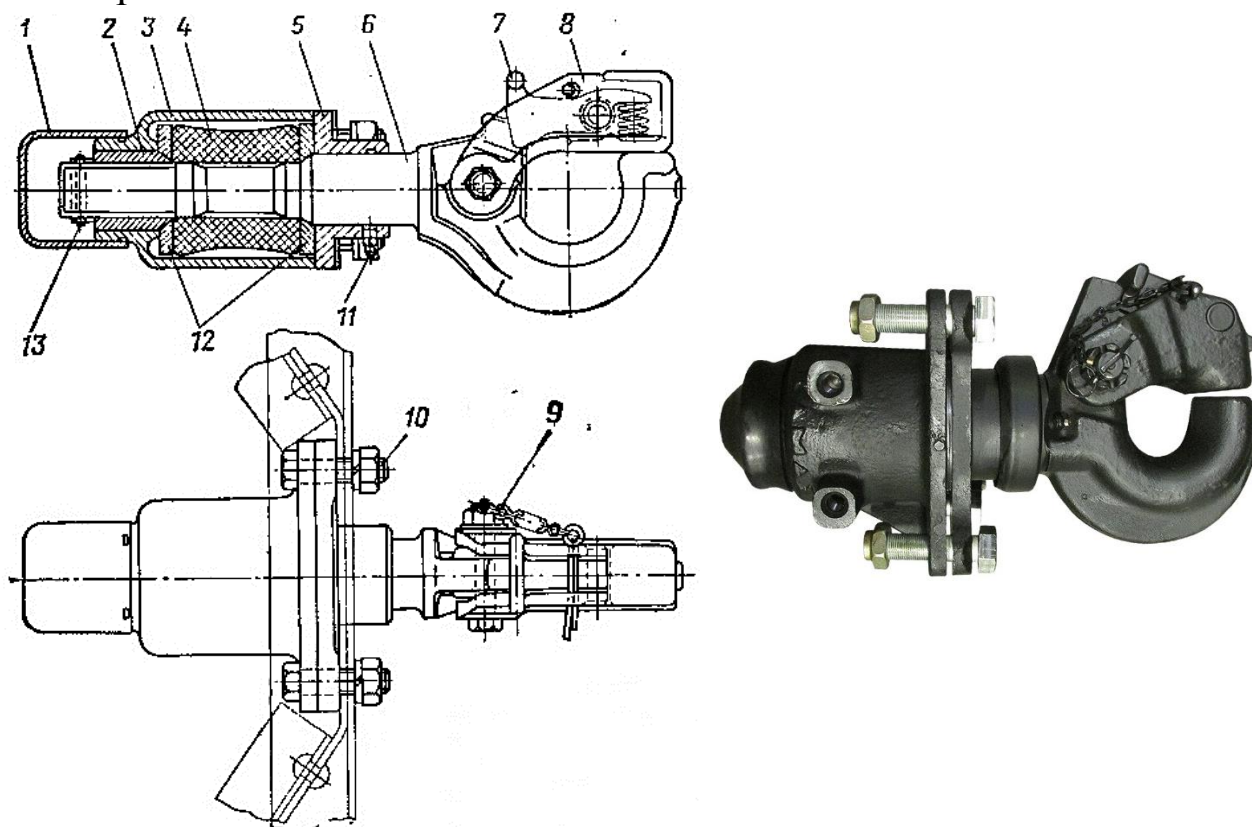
Буксирный прибор: 1 – колпак; 2 – опорная гайка; 3 – корпус; 4 – упругий элемент; 5 – кронштейн; 6 – буксирный крюк; 7 – собачка; 8 – защелка; 9 – цепочка; 10 – болт с гайкой; 11 – пресс-масленка; 12 – шайбы; 13 – шплинт
